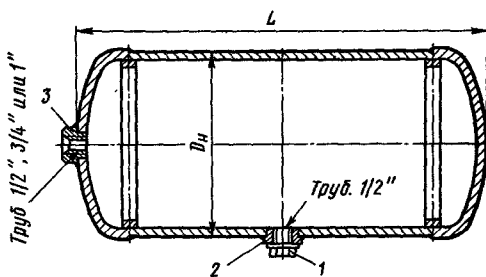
Запасной резервуар (ГОСТ 1561—75)
